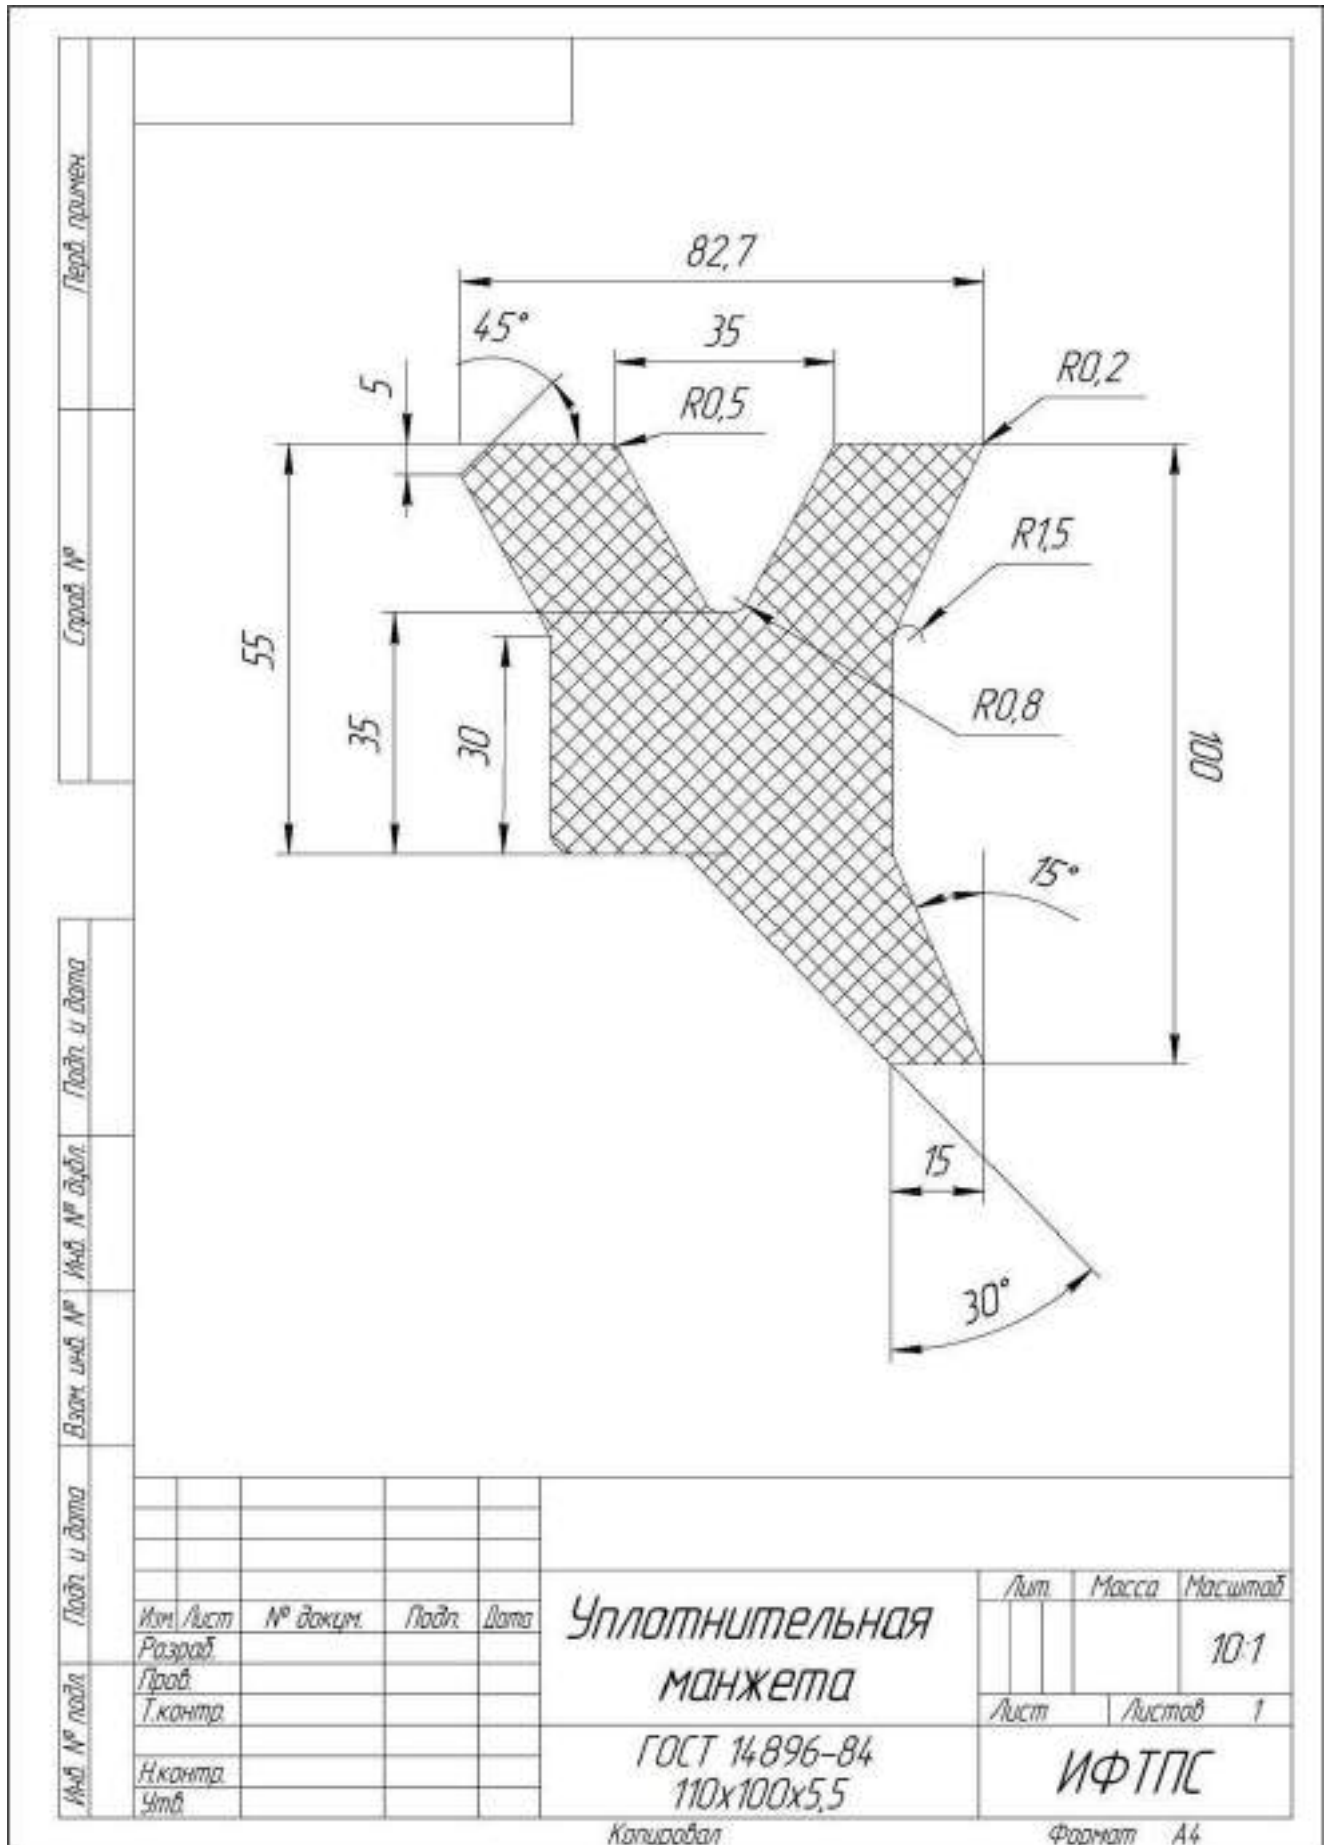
Чертеж пресс-формы для уплотнительной манжеты
